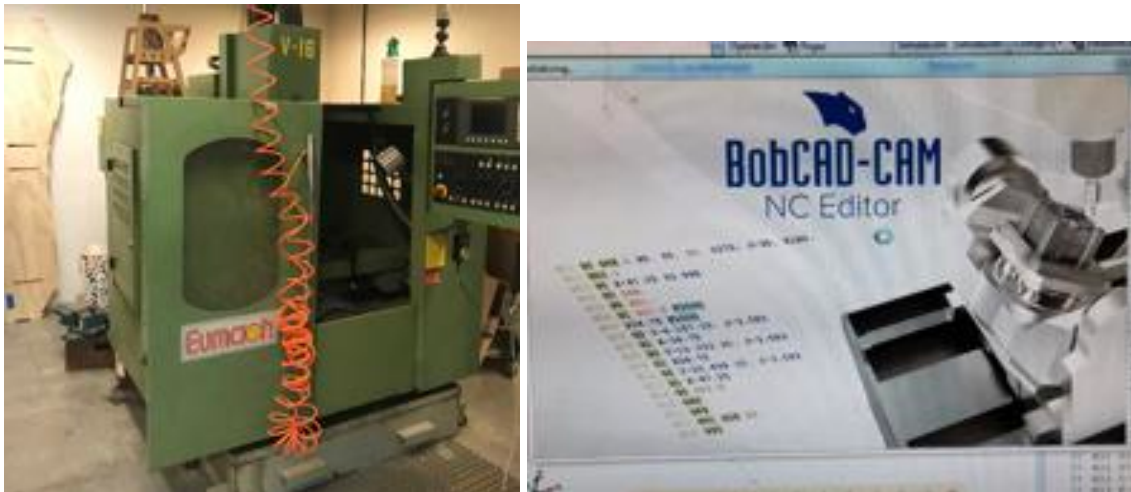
Izq. Máquina de CNC Eumach V-16, Der. Programa de CNC BobCAD-CAM.
